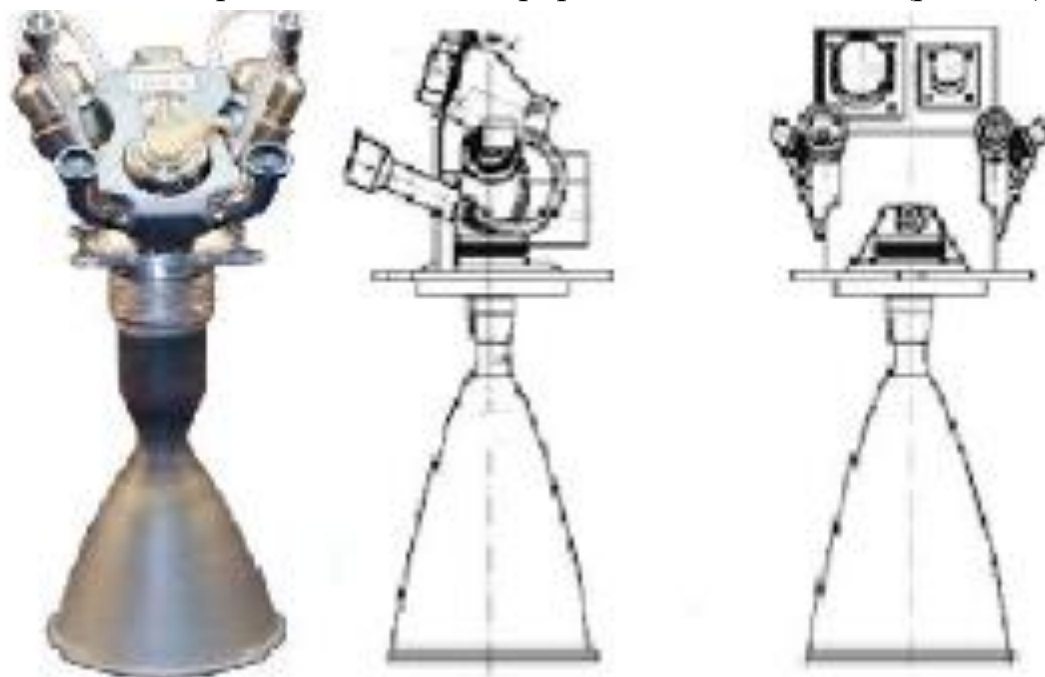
Общий вид двигательной установки 11Д428А-16
